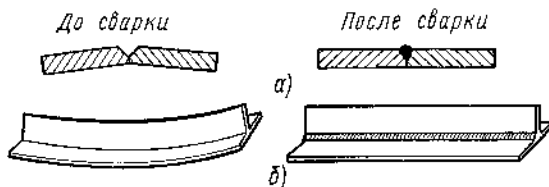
Обратные деформации и положение элементов изделия после сварки:
